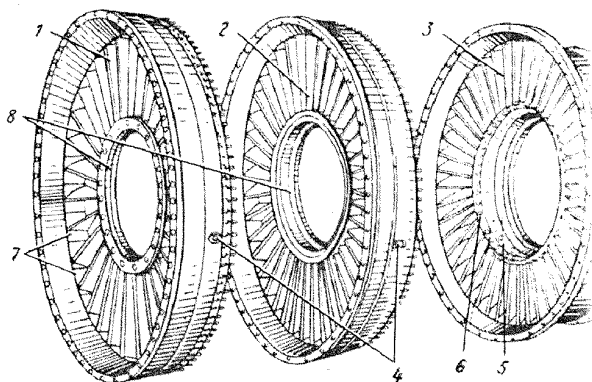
Корпуса КНД с направляющими аппаратами (НА): 1 - корпус с НА I ступени (33 лопатки); 2 - корпус с НА II ступени (33 лопатки); 3 - корпус с НА III ступени (94 лопатки); 4 - лопатки; 5 - внутренние кольца; 6 - крепеж; 7 - распорные вставки; 8 - кольца
